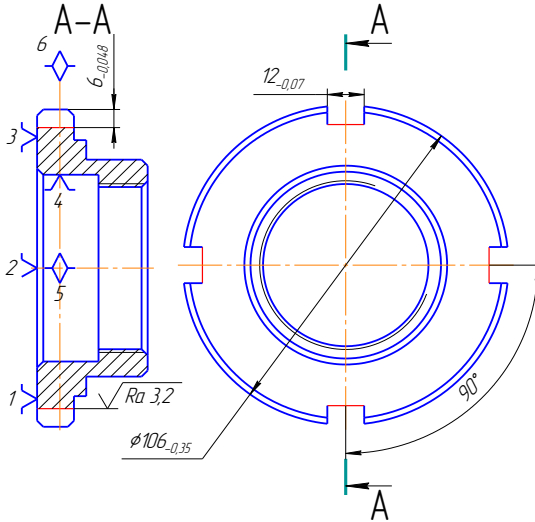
Технологический эскиз обработки для фрезерной операции 010.
